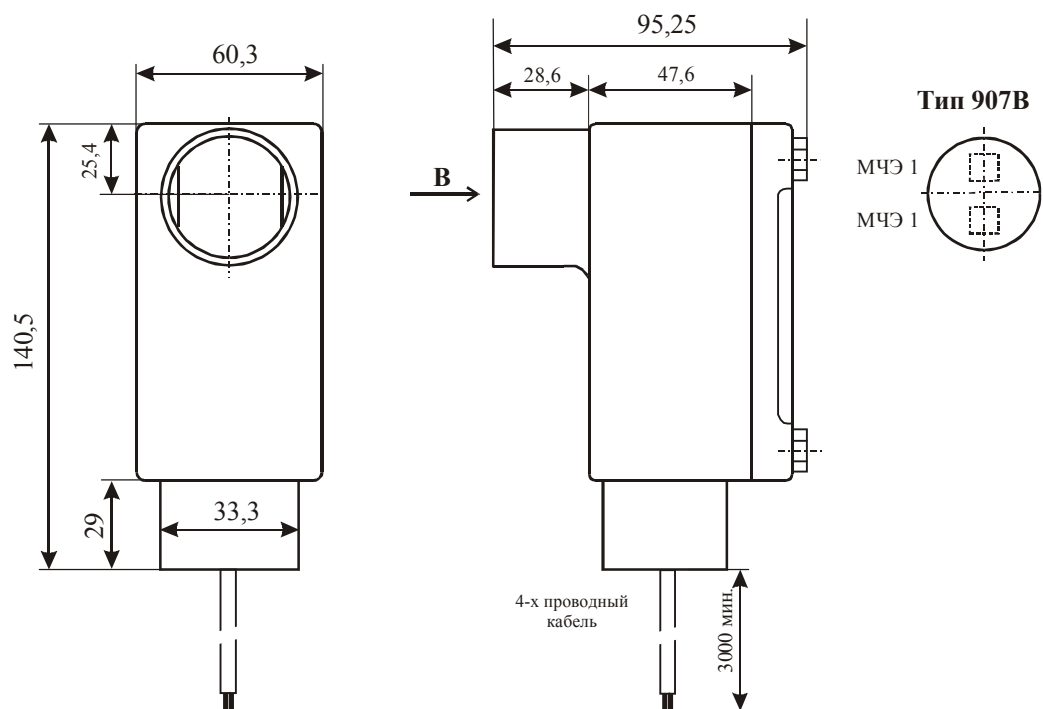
Внешний вид и габаритные размеры датчиков типа 931
